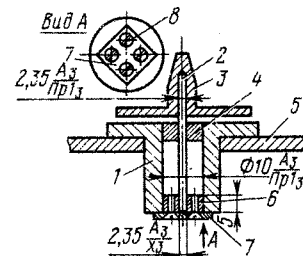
Узел вращения диска: 1 — втулка, Д16-Т; 2 — валик, сталь инструментальная, закалить, полировать; 3 — шпиндель, Ст. 45, полировать; 4 — подшипник верхний БрМцЗ-1, запрессовать в дет. 1; 5 — панель проигрывателя; 6 — подшипник нижний, БрМцЗ-1, запрессовать в дет. 1; 7 — пластина, капронлон; 8 — винт М2 × 5, 4 шт.
